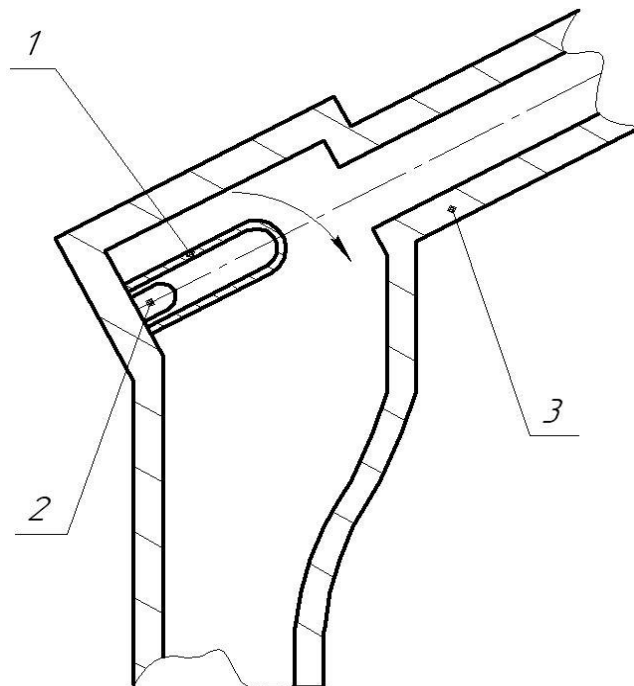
Схема орієнтування заготовки за допомогою упорного гвинта
